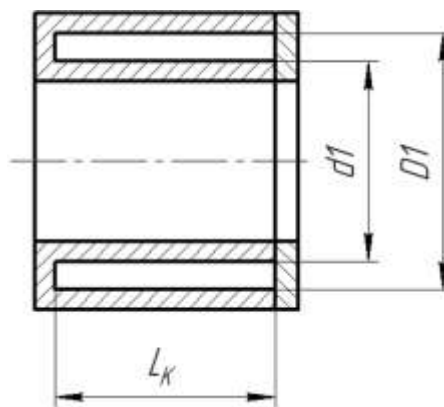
Схема рабочей камеры подшипника скольжения
